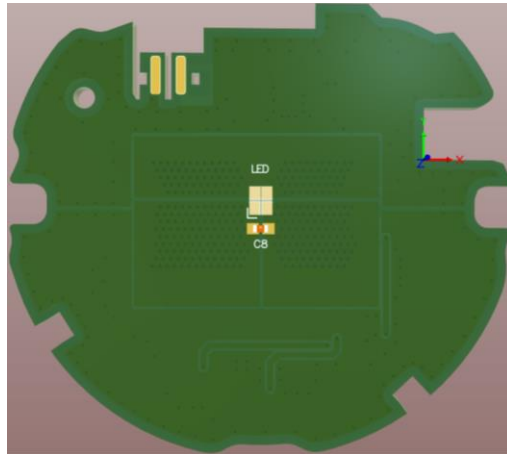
PCB Üzerine Tüm Komponentlerin Yerleşimi
